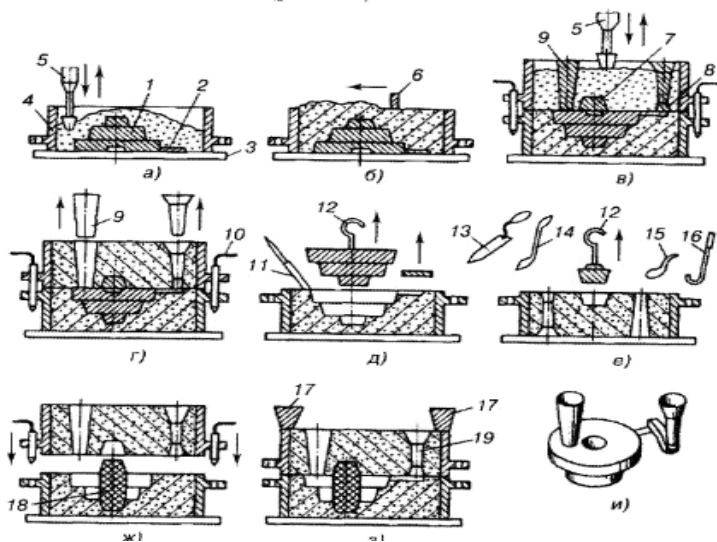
Основные операции при изготовлении песчано-глинистой формы ручной формовкой: *а* - формовка нижней опоки; *б* - срезание излишков смеси; *в* - формовка верхней полуформы; *г* - извлечение моделей стояка и прибыли; *д, е* - извлечение моделей отливки и отделка формы; *ж* - установка стержня и сборка формы; *з* - наложение груза; *и* - отливка с литниково-питающей системой; *1, 7* - нижняя и верхняя половинки модели отливки; *2* - модель питателя; *3* - подмодельная плита; *4* - опока; *5* - трамбовка; *6* - линейка; *8* - модель стояка; *9* - модель прибыли; *10* - штырь; *11* - кисть; *12, 16* - крючок; *13* - гладилка; *14* - ланцет; *15* - ложечка; *17* - груз; *18* - стержень; *19* - литниковая система
